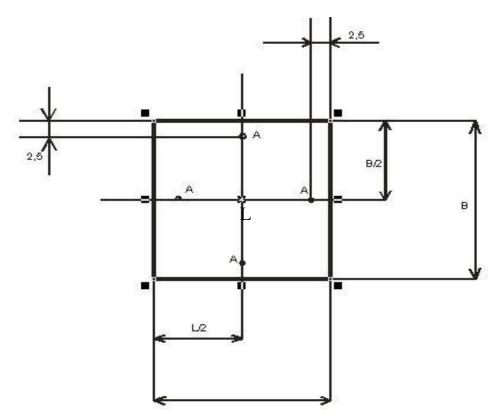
Схема разметки образца при определении плотности ДСтП: l – длина образца; b – ширина образца; А – точки измерения
